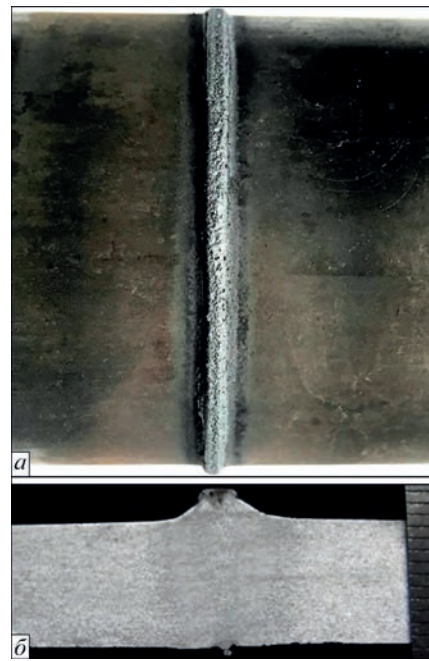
Формування зварного з'єднання з контрольованою осадкою: *а* – загальний вигляд зварного з'єднання; *б* – поперечний переріз зварного з'єднання
